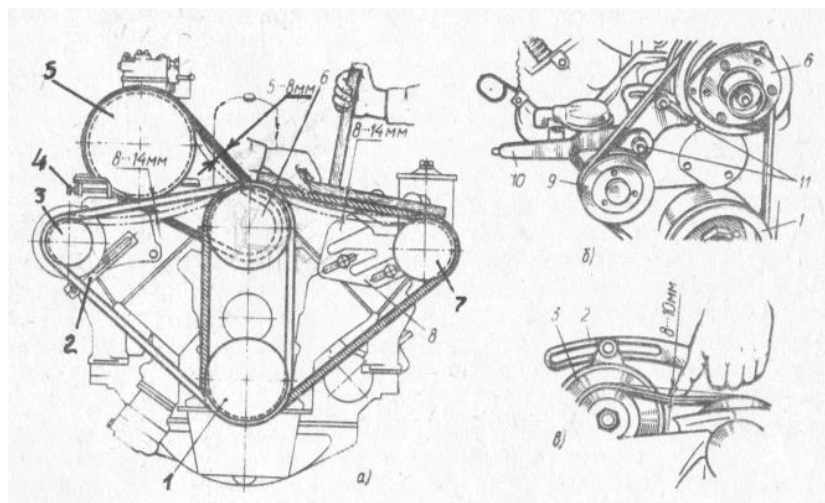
Контроль и регулировка натяжения приводных ремней двигателей автомобилей:
